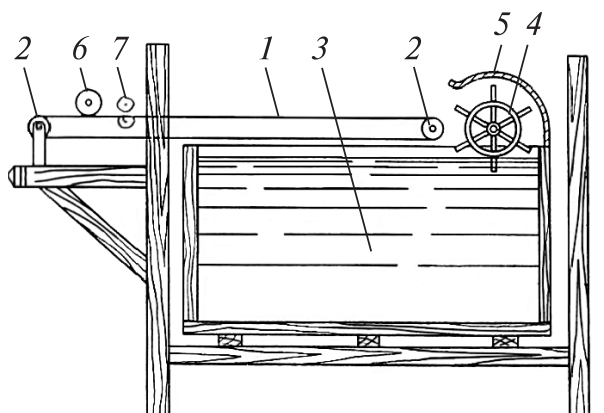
«Самочерпка» Робера: 1 — сетка; 2 — натяжные валики; 3 — черпальный чан; 4 — черпальное колесо; 5 — отражательный щиток; 6 — пресс; 7 — накат
